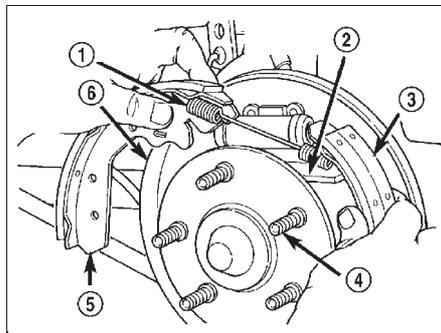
Снятие/установка тормозных колодок. 1 - верхняя возвратная пружина, 2 - винт автоматического регулятора, 3 - ведомая тормозная колодка, 4 - шпильки крепления колес, 5 - ведущая тормозная колодка, 6 - опорная плита.
